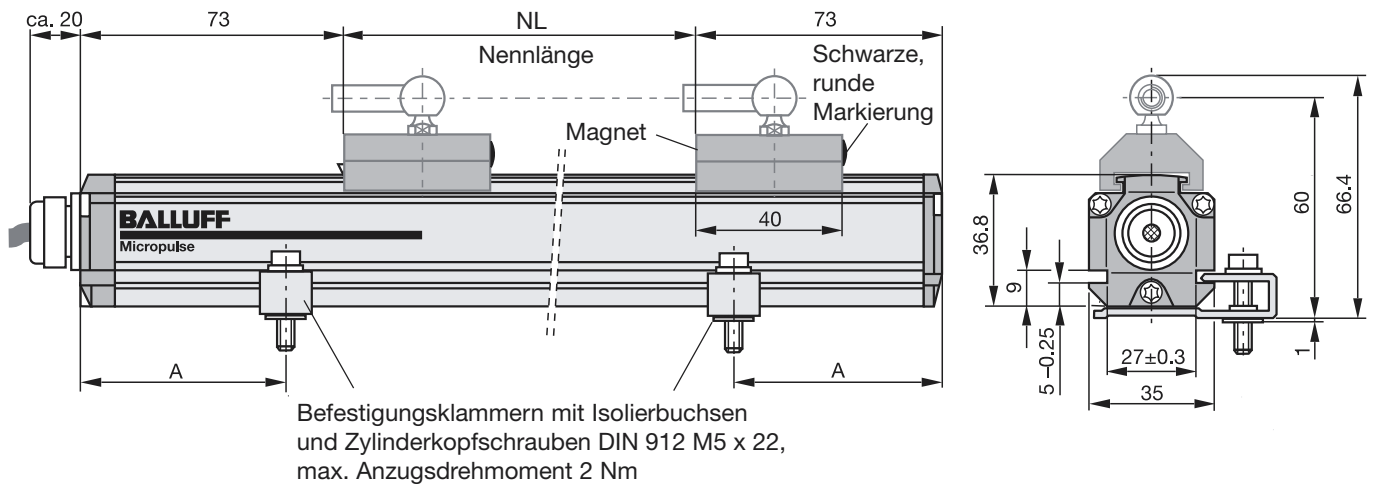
Maßzeichnung (Wegaufnehmer BTL5...P-KA.. mit geführtem Positionsgeber BTL5-F-2814-1S)
